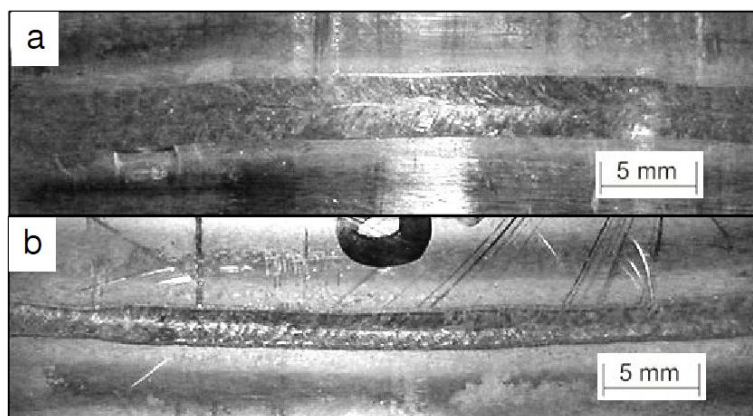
Solda de união de tubos com corrente contínua constante, em (a) face e em (b) raiz da solda. Parâmetros: I: 36A e Vs: 2 mm/s (12 cm/min).
